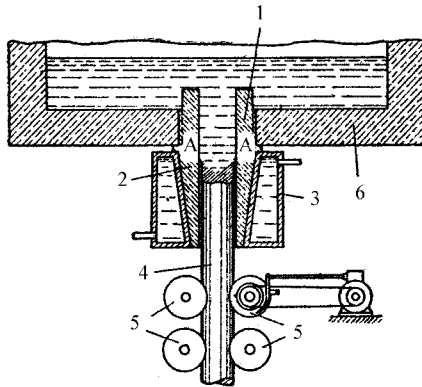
Встроенный в печь кристаллизатор для получения медной непрерывнолитой заготовки [161]
